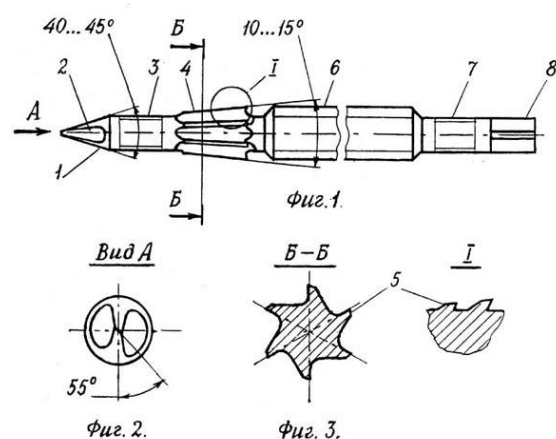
Стержень для выполнения наружного чрескостного остеосинтеза: 1 - заостренный на конус конец; 2 - две плоские грани; 3 - цилиндрический участок с метрической резьбой; 4 - заборный конус; 5 - режущие зубья; 6 - резьбовой участок с упорной резьбой; 7 - цилиндрический участок с метрической резьбой; 8 - хвостовик под ключ с квадратным сечением
